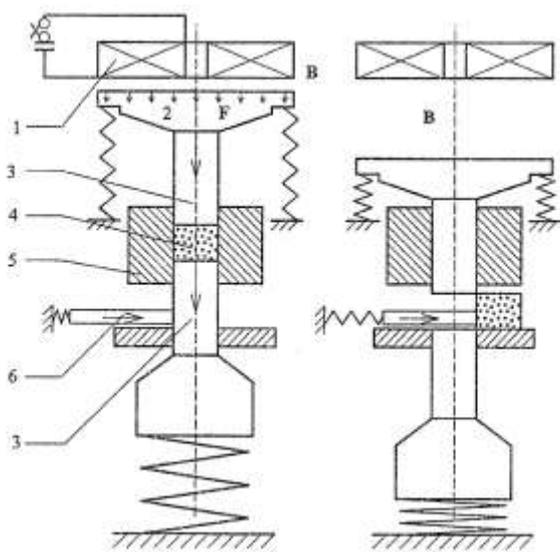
Схема одноосного магнитно-импульсного прессования нанопорошков: а – стадия сжатия; б – стадия выемки готового образца, 1 – индуктор; 2 – концентратор; 3 – верхний и нижний пуансоны; 5 – матрица; 6 – устройство выемки образца
